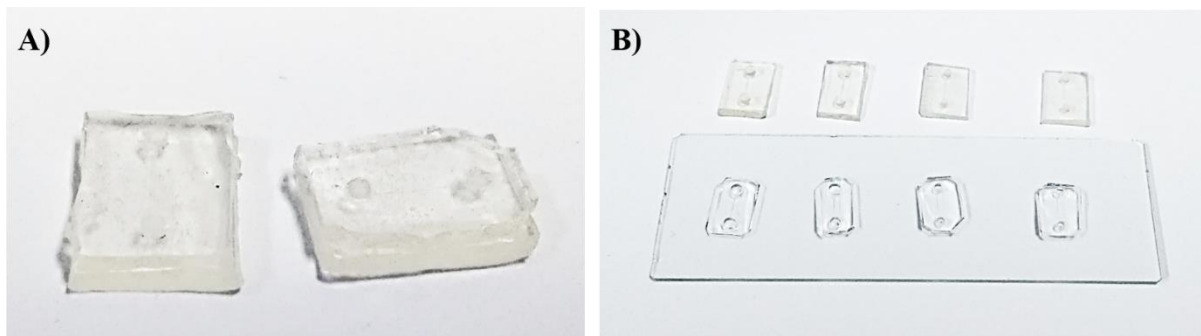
A) Moldes de resina epóxica con PDMS antes de desmoldar. B) PDMS ensamblado en sustrato de vidrio.
